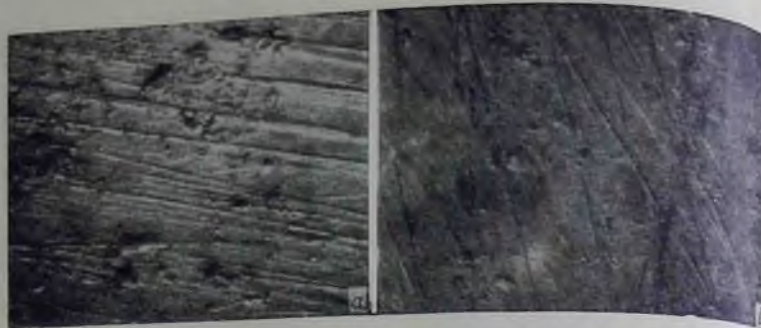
Изношенная поверхность зуба ковша экскаватора ЗЭР-500-2
